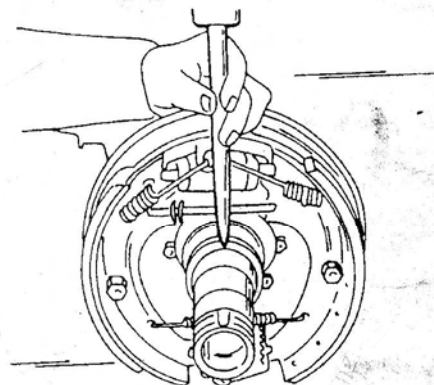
Для снятия распорного кольца его нужно расколоть резцом.
